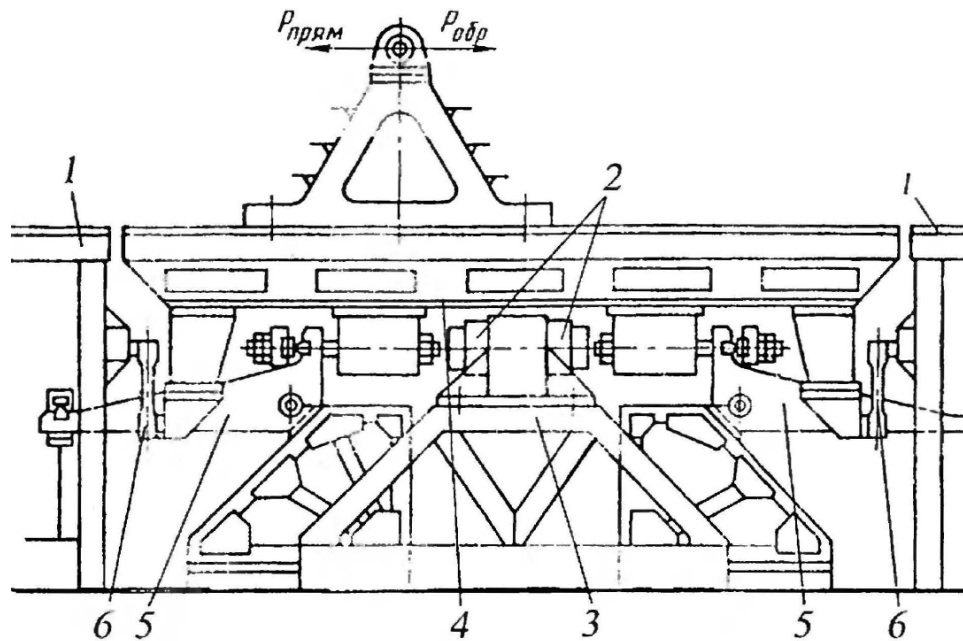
Конструкція силівимірювального пристрою з підвіскою динамометричної платформи на пружних опорах:
